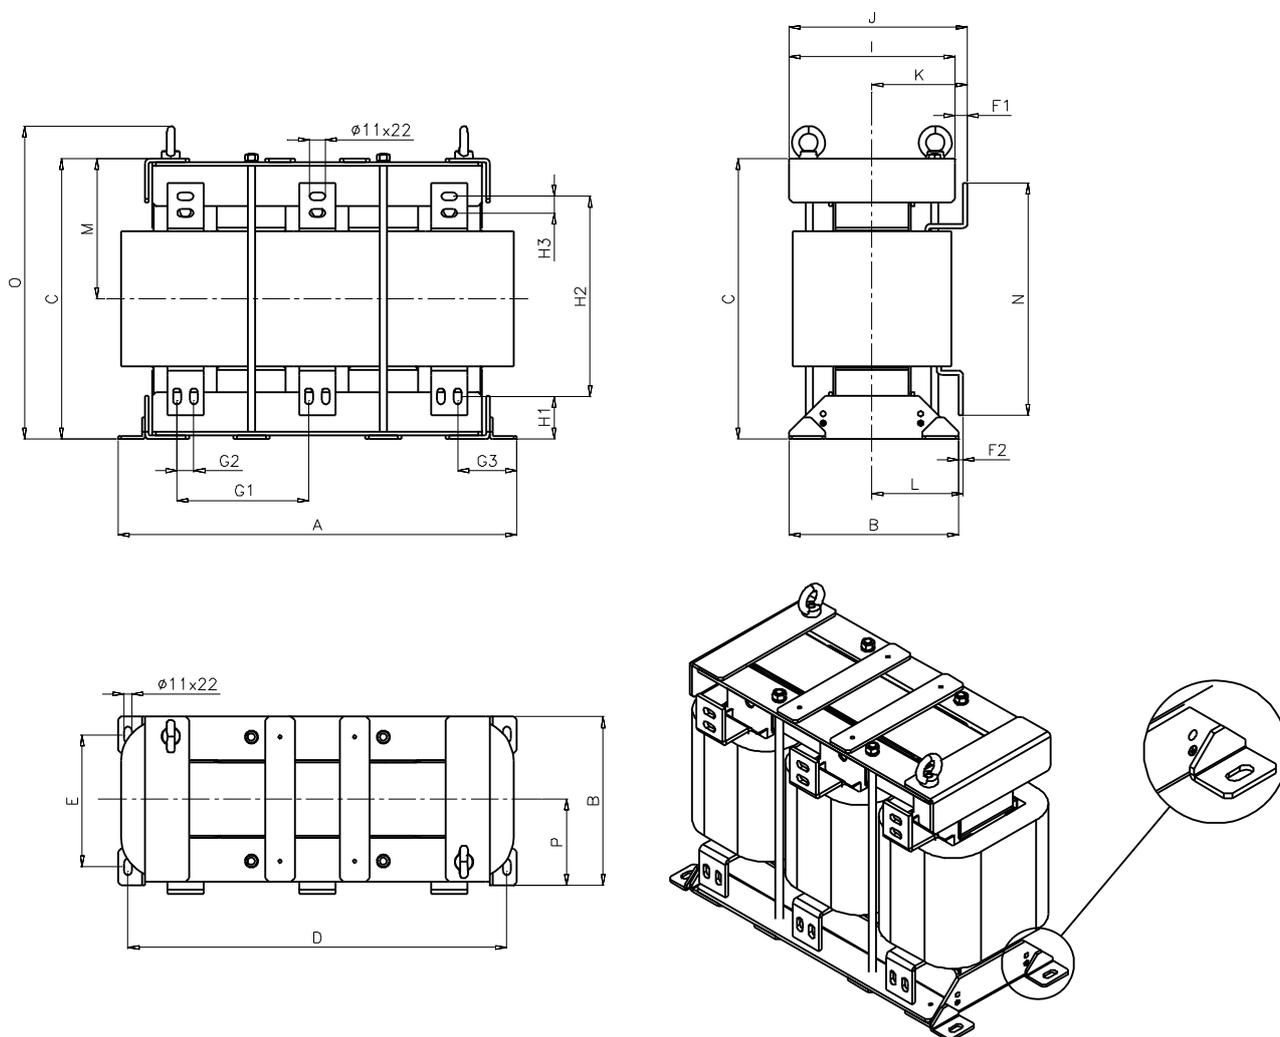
Disegno quotato bobina di rete 6SL3000-0EE41-4AA0
